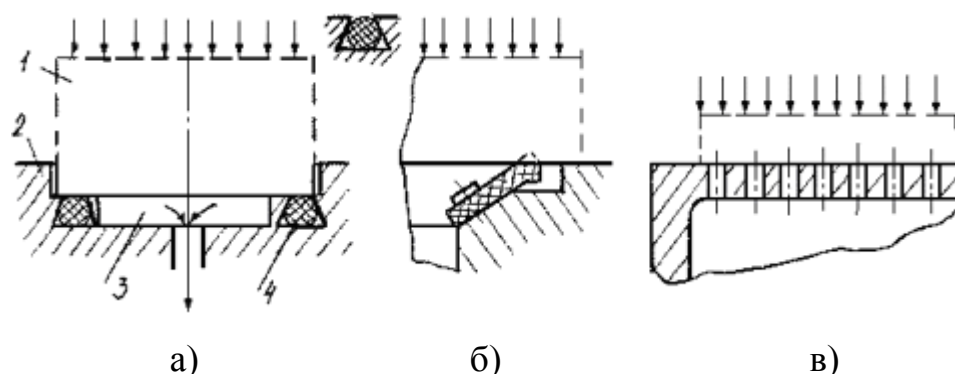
Закріплення заготовки за допомогою вакуумного приводу
